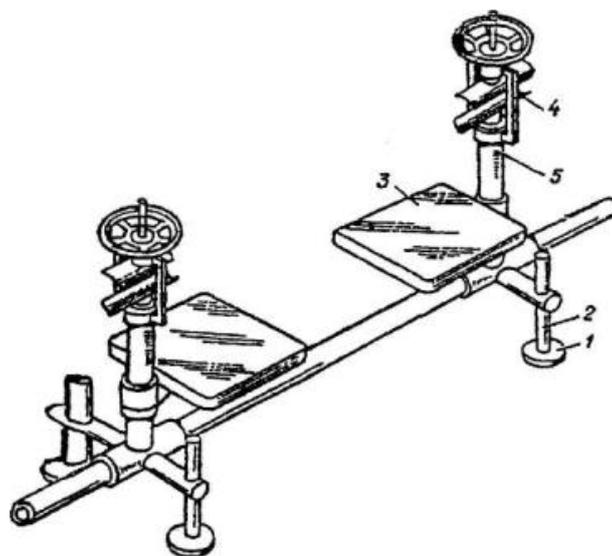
Приспособление для монтажа соединительных муфт: 1 - диск упорный; 2 - ножка; 3 - лоток; 4 - уголок; 5 - стойка
